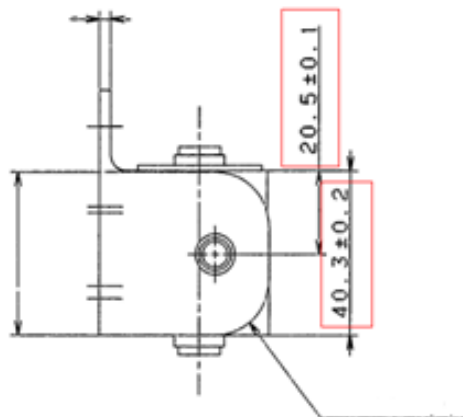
Representação de cotas toleranciadas em desenho técnico<sup>38</sup>.
